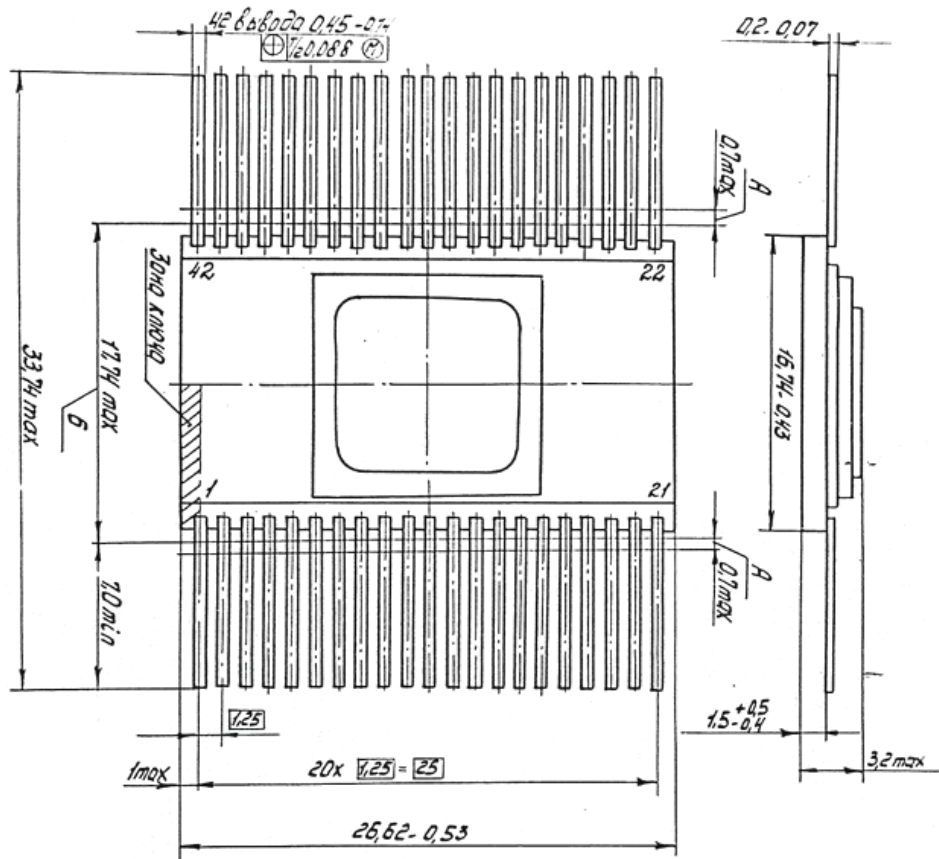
Габаритный чертеж корпуса 429.42-5
